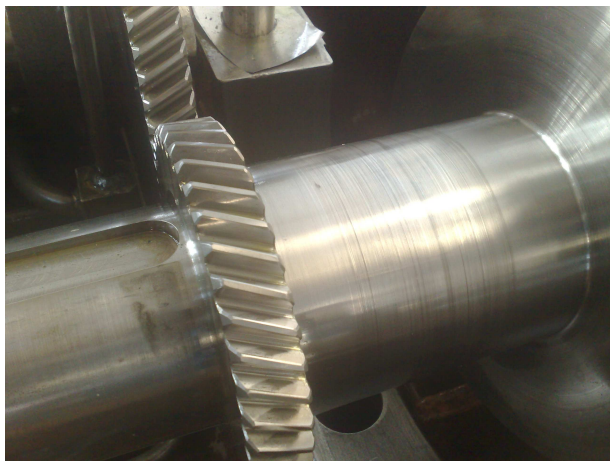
Состояние подшипниковых несущих поверхностей ротора без упрочнения
